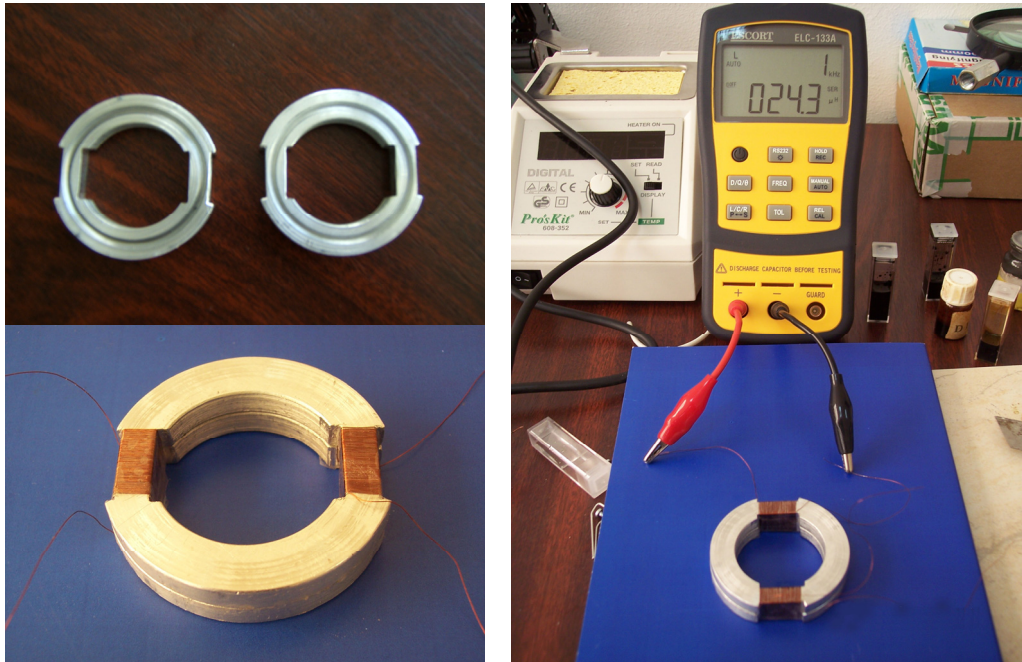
Inclinatorul pentru determinarea poziției într-un plan perpendicular pe planul celor două capete de sudare
